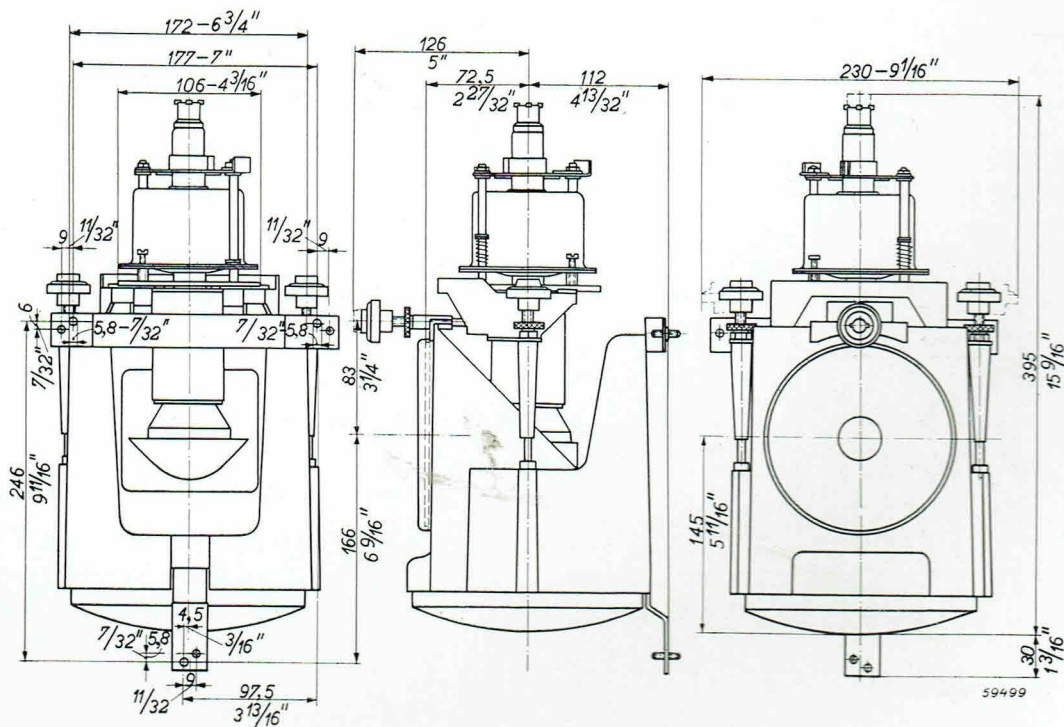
Dessins cotés de la boîte optique type 10950.
